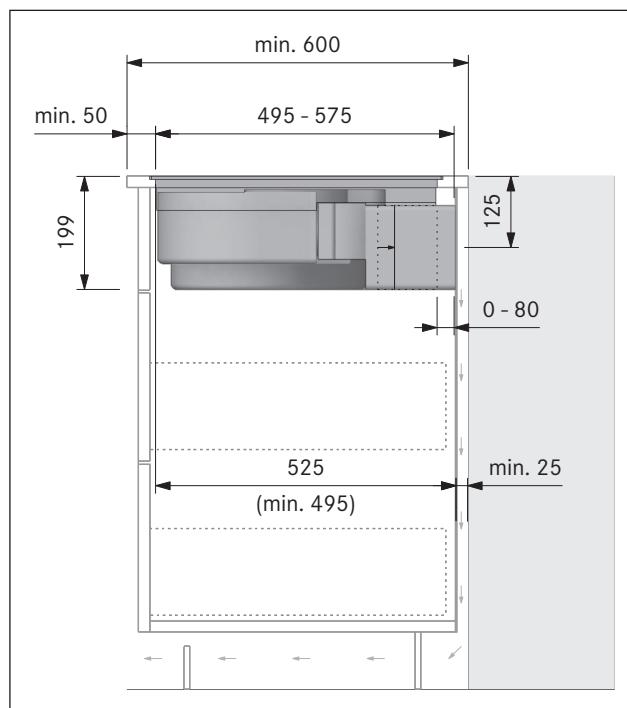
Dimensioni di montaggio con sistema filtrante, variante di montaggio A
